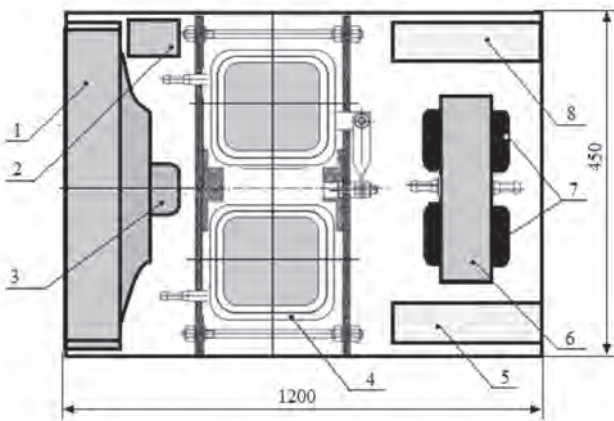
Компоновка основных узлов (вид сверху) СШН:
